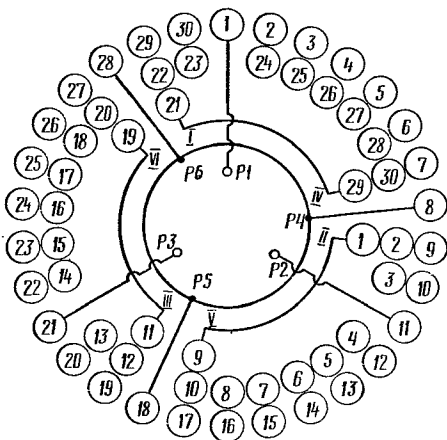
Торцевая схема обмотки ротора с дробным числом пазов на полюс и фазу
